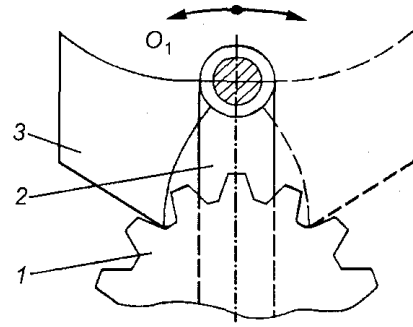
Реверсивний храповий механізм: 1 - храповик; 2 - провідний важіль; 3 - собачка
